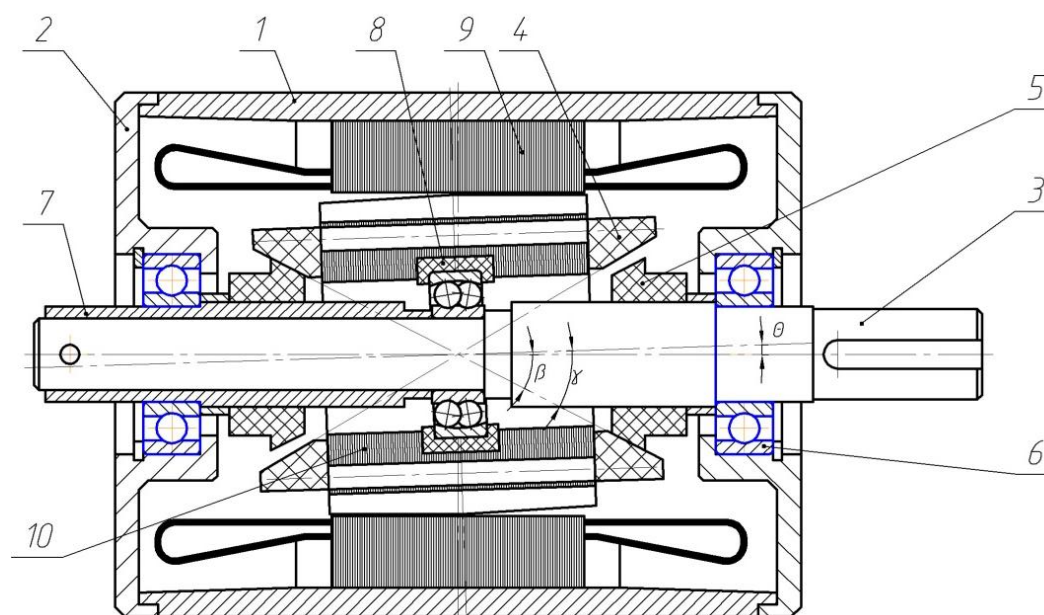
Общий вид конструкции прецессионного магнитного редуктора с фрикционным зацеплением
